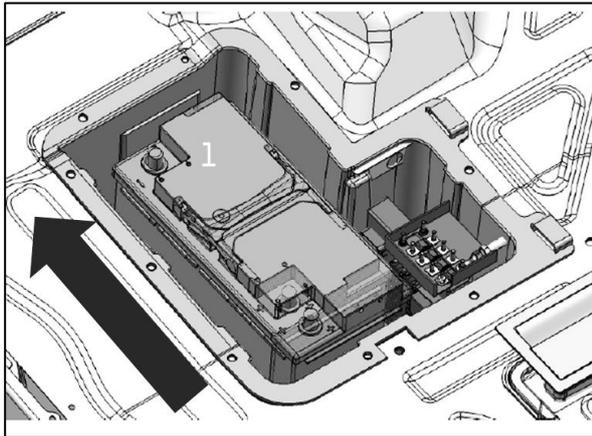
Position de montage de la batterie principale, plancher à gauche
